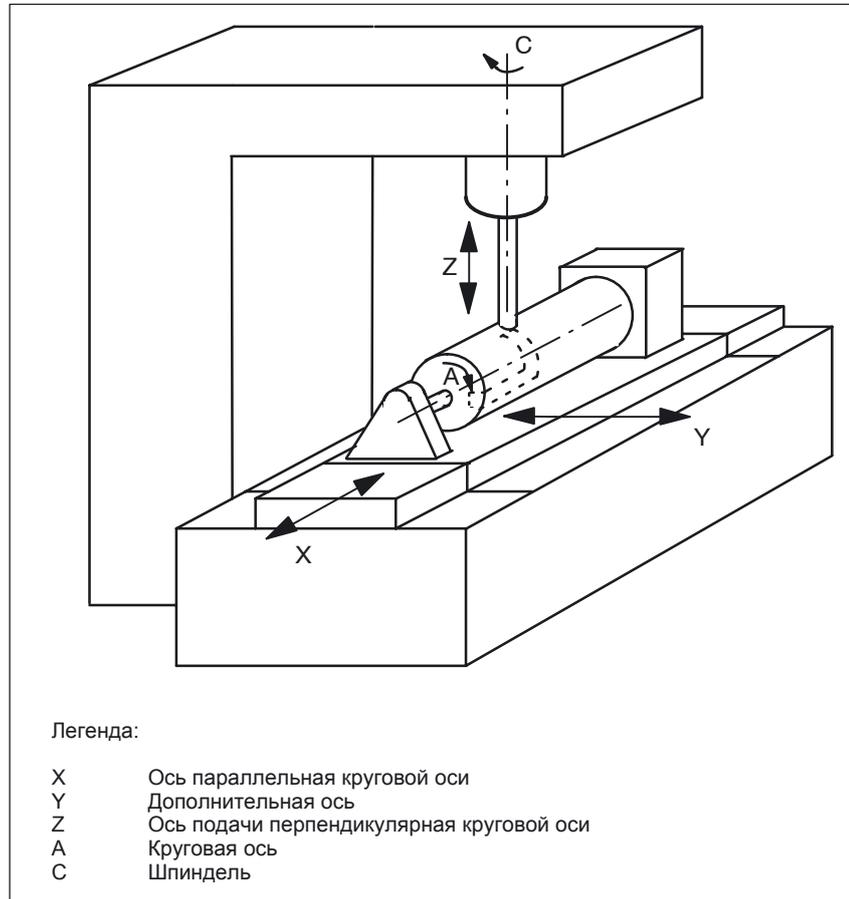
Обработка паза в боковой поверхности цилиндра с X–C–Z–кинематикой
